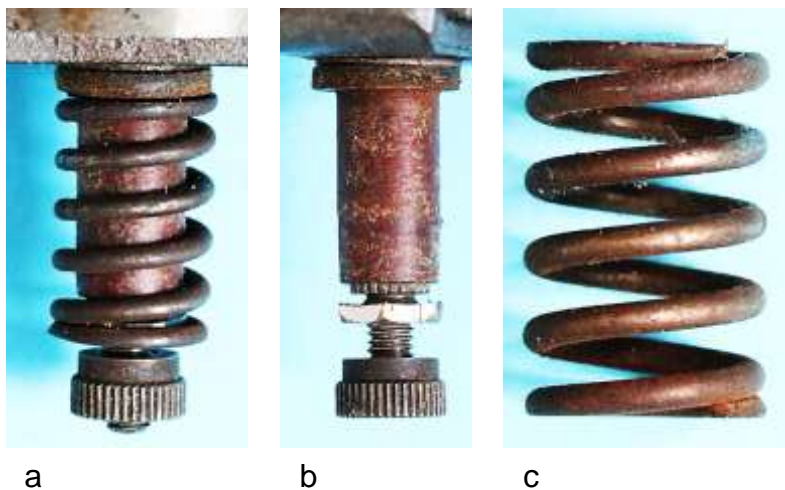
Kabelanschlussbolzen mit Druckfeder:
